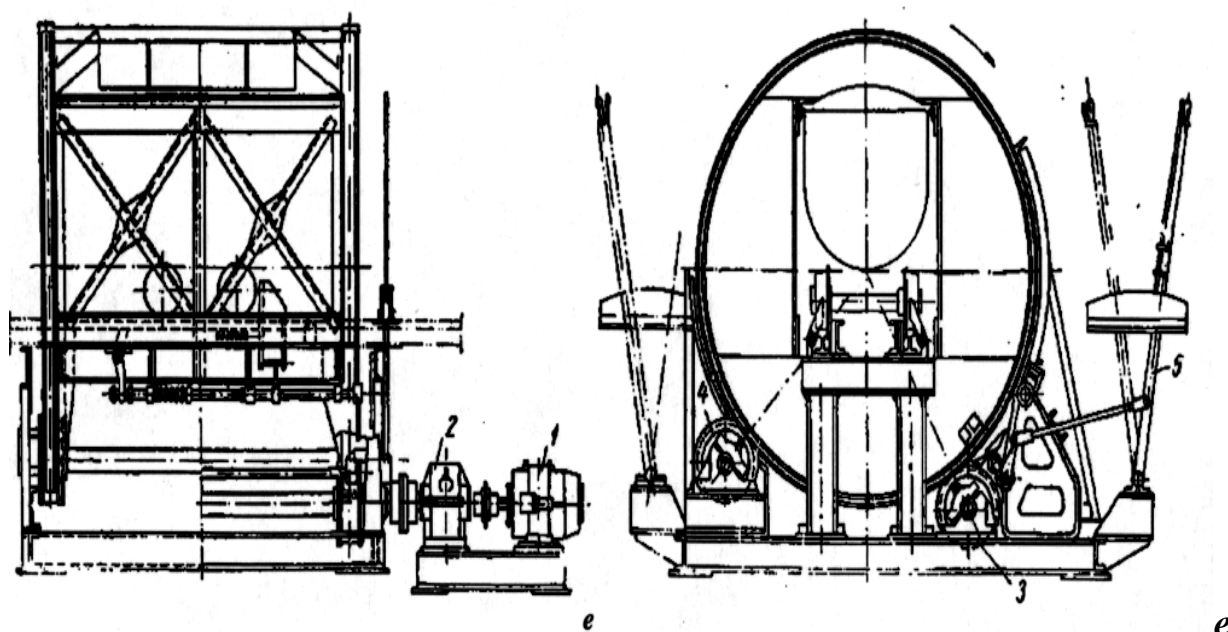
Круговой опрокидыватель для нерасщепленных вагонеток: 1 – электродвигатель; 2 – редуктор ; 3 – приводные ролики; 4 – опорные ролики ; 5 – рукоятка управления
